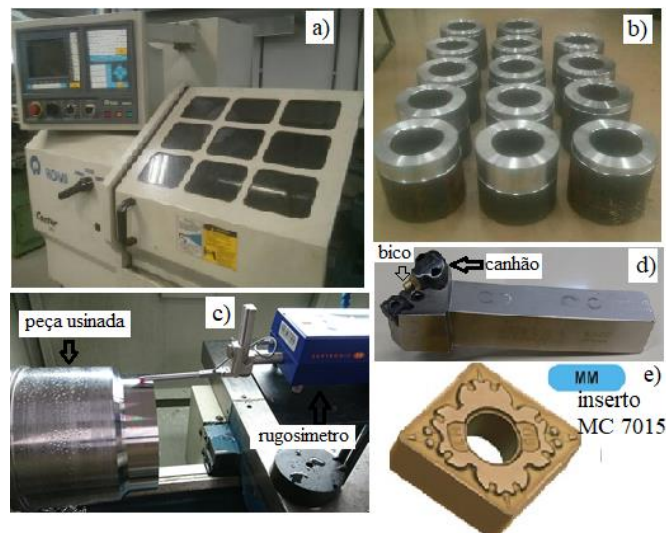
Equipamentos e materiais: (a) torno Centur 30S, (b) corpos de prova, (c) medição da rugosidade, (d) porta-ferramenta e (e) inserto de metal duro MC 7015.
